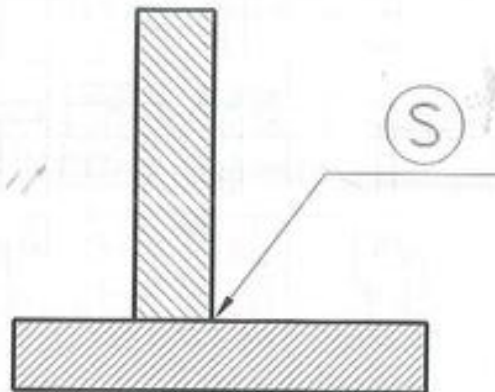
Representación de las uniones soldadas sin especificar.
